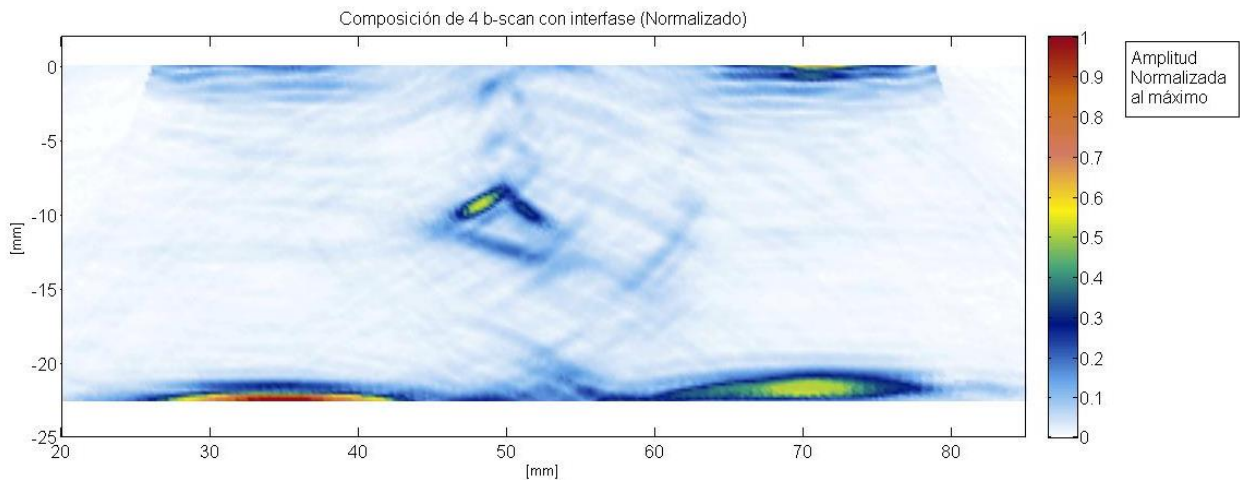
Composición con reflexión especular de 4 B-Scans de la probeta de acero inoxidable austenítico soldada.
